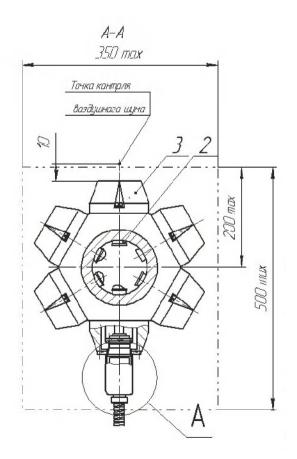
Первичный преобразователь ПП6-Р (соединение сварное)
